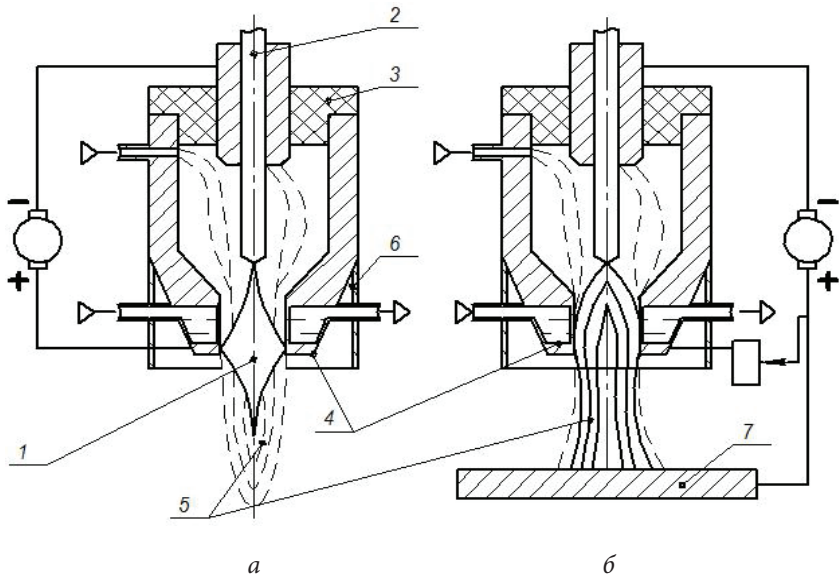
Схемы получения плазменной струи, выделенной из дуги (а), и плазменной дуги, совмещенной с плазменной струей (б): 1 — дуга; 2 — вольфрамовый электрод; 3 — керамическая прокладка; 4 — корпус горелки; 5 — сопло; 6 — плазменная струя; 7 — заготовка
